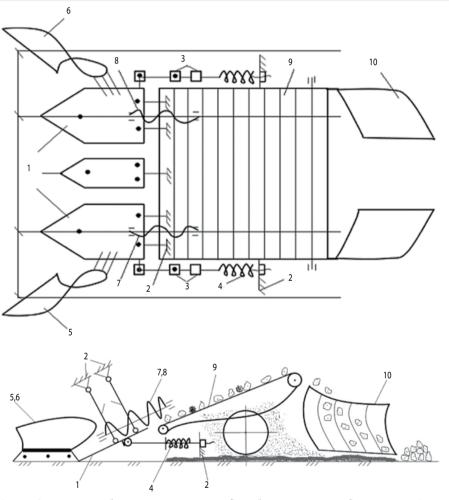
Схема энергосберегающего копателя для уборки лука: 1 — подкапывающий лемех; 2 — рама; 3 — подвеска; 4 — пружина; 5, 6 — лево- и правооборачивающие отвалы; 7, 8 — шнеки; 9 — элеватор; 10 — лоток
